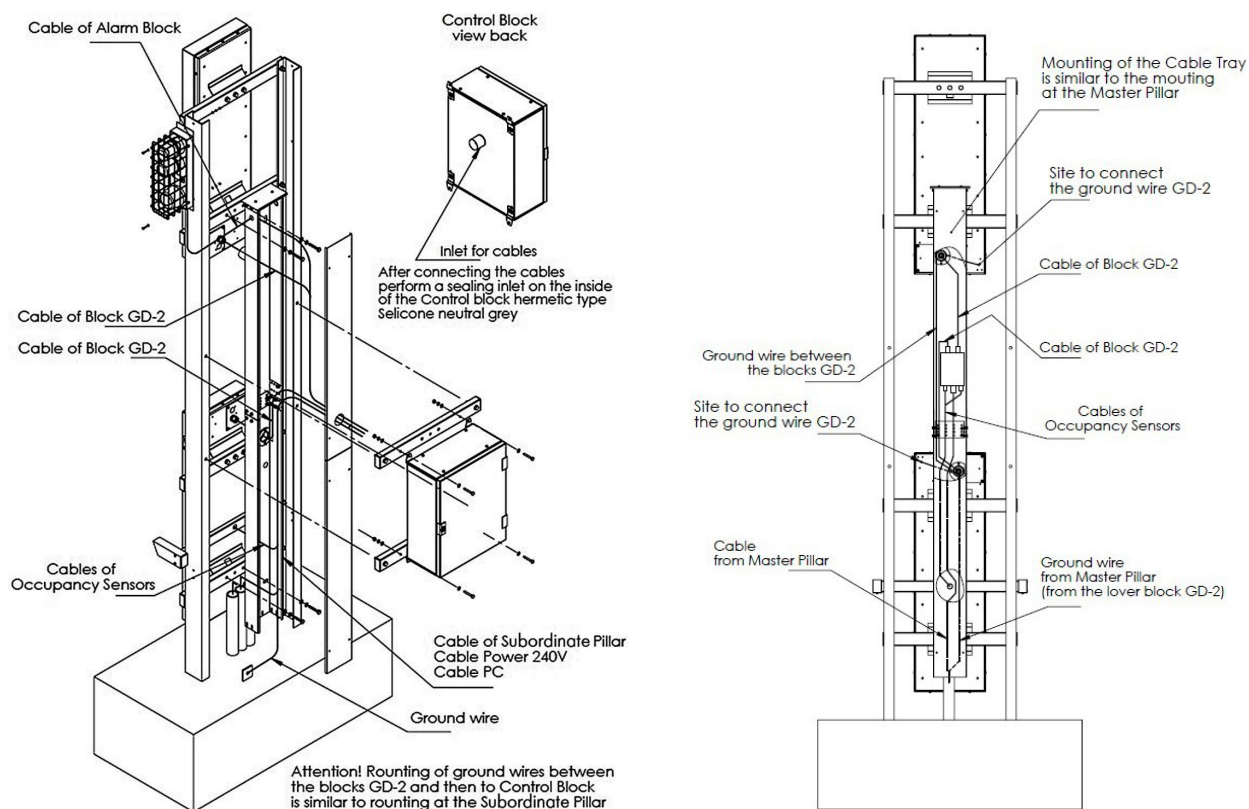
Montaje del pilar maestro (a) y el pilar subordinado (b)
